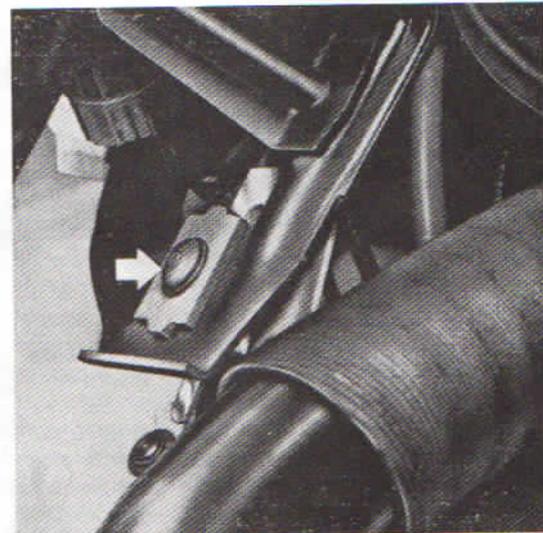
Schraubenkopf der Abreißschraube für hintere Abreißschlittenbefestigung abböhen
